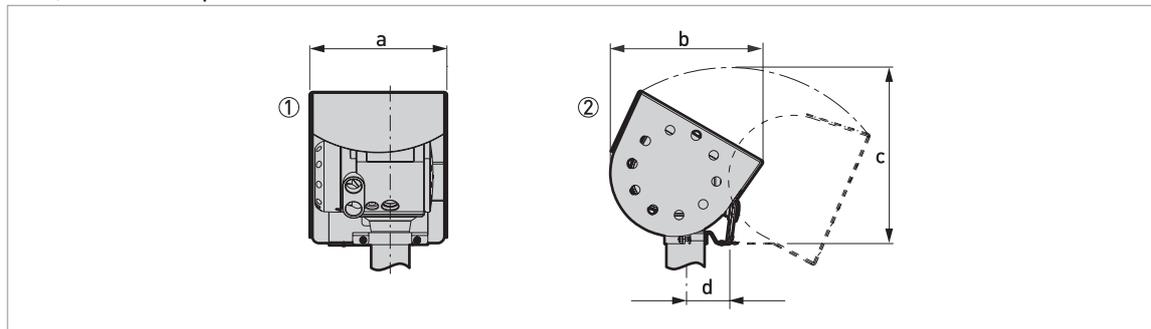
Габаритные размеры опционального защитного козырька
